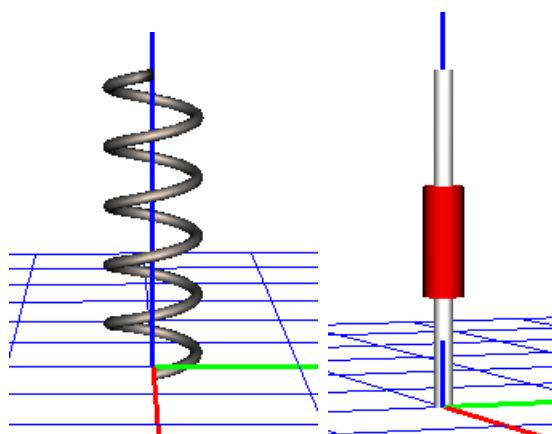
Примеры упрощенного ГО для изображения цилиндрической пружины и гасителя колебаний
